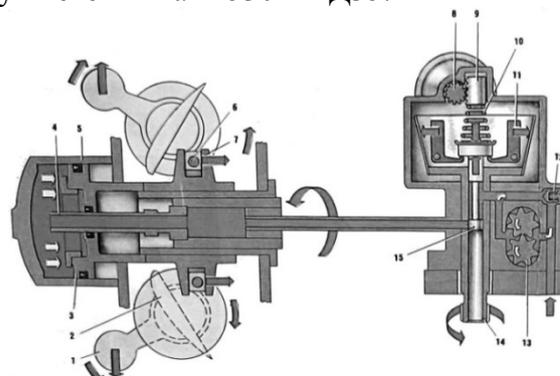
Винт В-530ТА-Д35: 1 – противовес; 2 – лопасть винта; 3 – поршень; 4 – штицер; 5 – цилиндр винта; 6 – палец; 7 – поводок; 8 – шестерня валика ручного управления; 9 – рейка; 10 – пружина регулятора; 11 – грузики регулятора; 12 – клапан редукционный; 13 – маслонасос; 14 – валок регулятора ведущий; 15 – золотник
